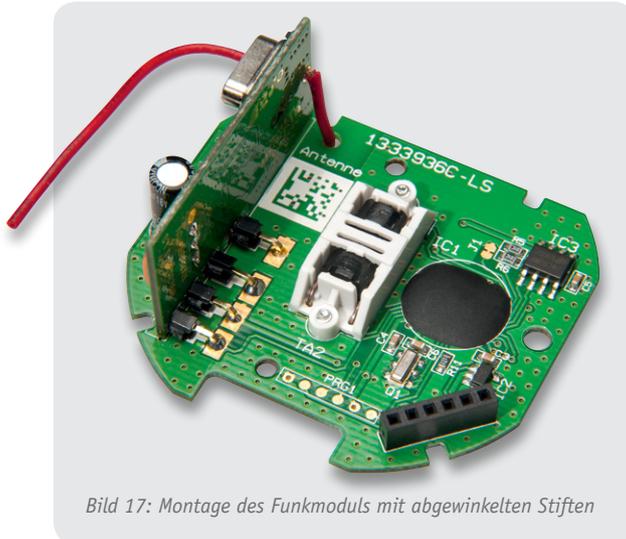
Montage des Funkmoduls mit abgewinkelten Stiften
